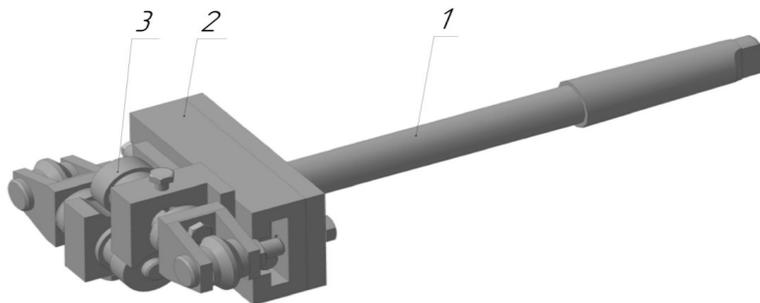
Двухроликковая инструментальная державка для ЭМУ отверстий большого диаметра
